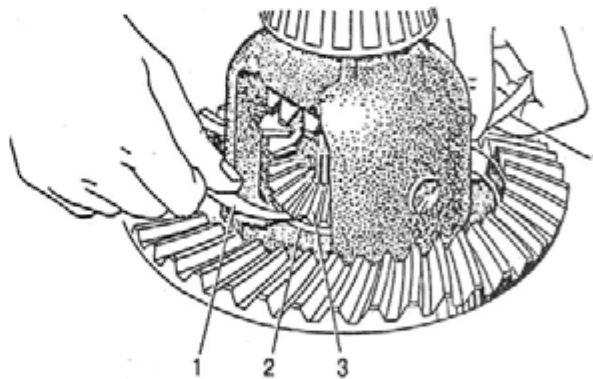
Проверка зазора полуосевых шестерен в дифференциале:
